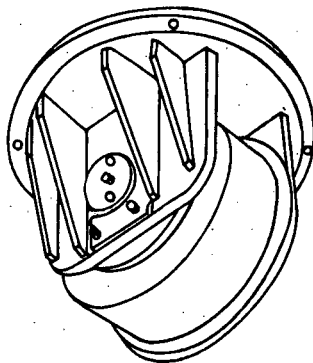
GUIA SOLDADA NO FUNDO DO TANQUE
